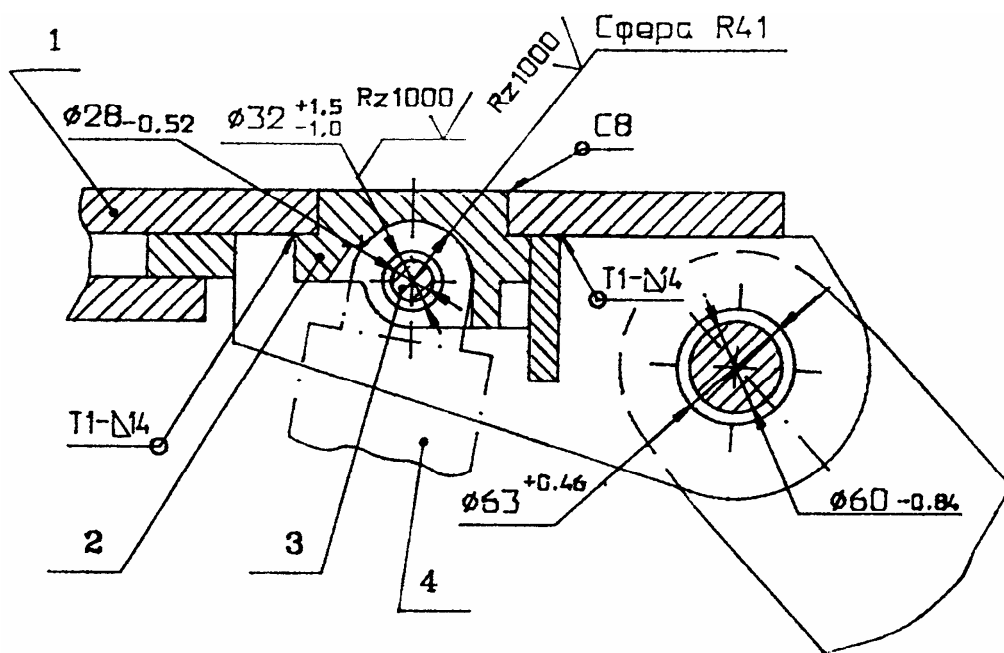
Соединение перекрытия с гидростойкой секции крени КД90
